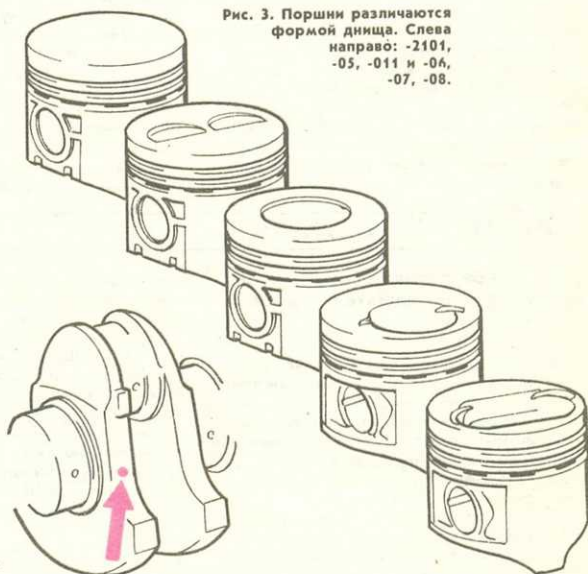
Поршни различаются формой днища. Слева направо: -2101, -05, -011 и -06, -07, -08.
